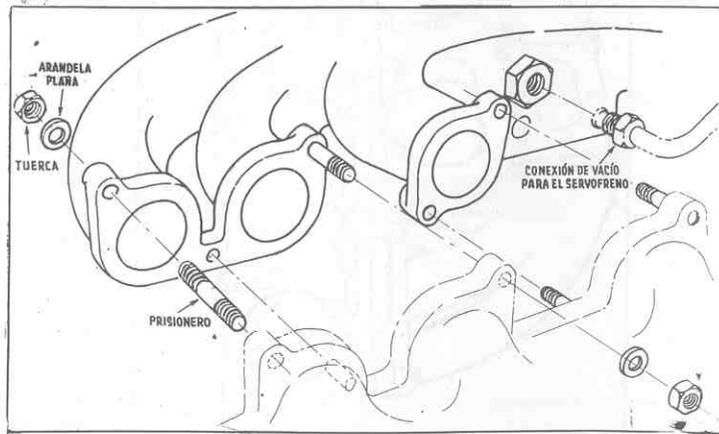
, detalle 2.— Disposición de los prisioneros de sujeción.
